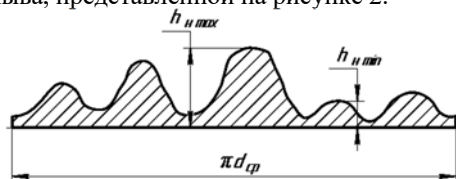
Схематическое представление развертки профиля сечения режущей кромки напыля металла по краю лунки
